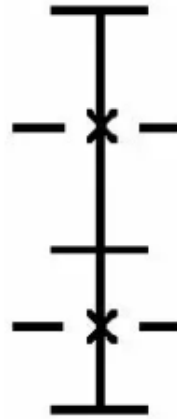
Кинематическая схема цилиндрического редуктора с внешним зацеплением
